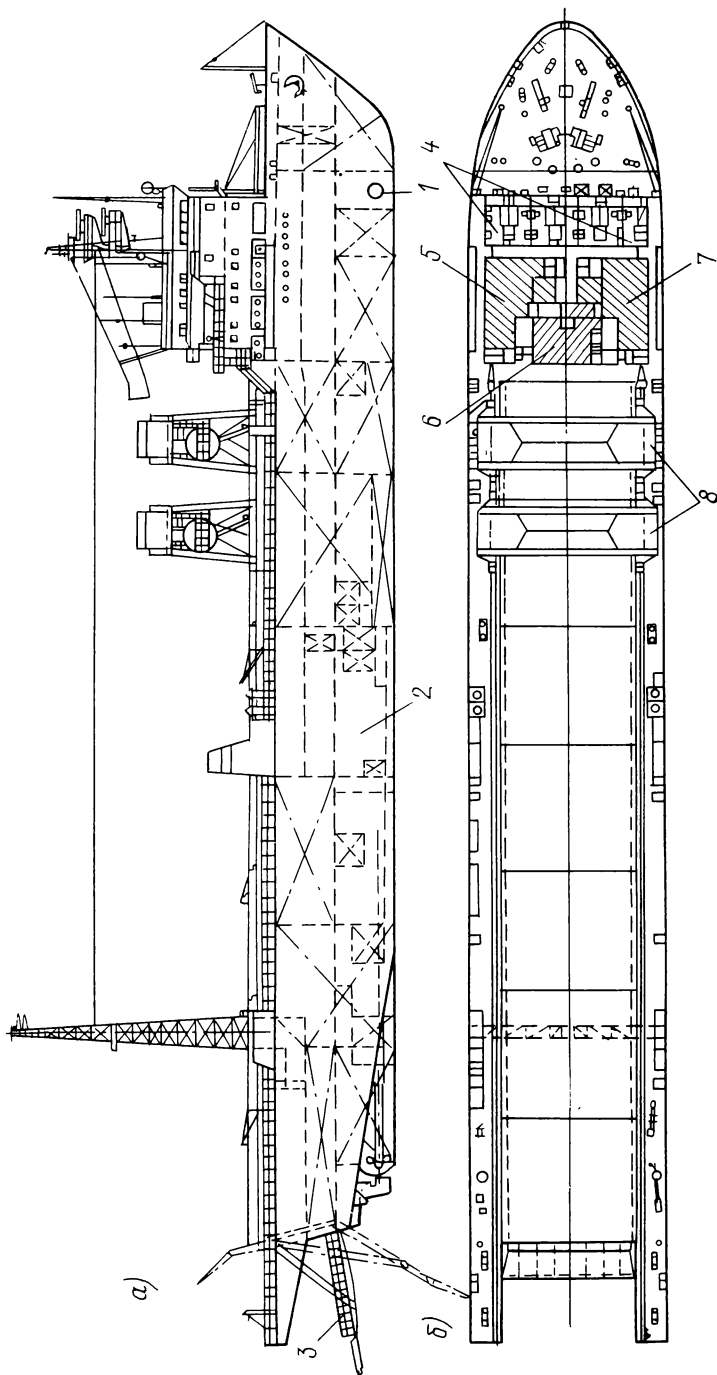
Общее расположение судна: а — боковой вид; б — план верхней палубы.
